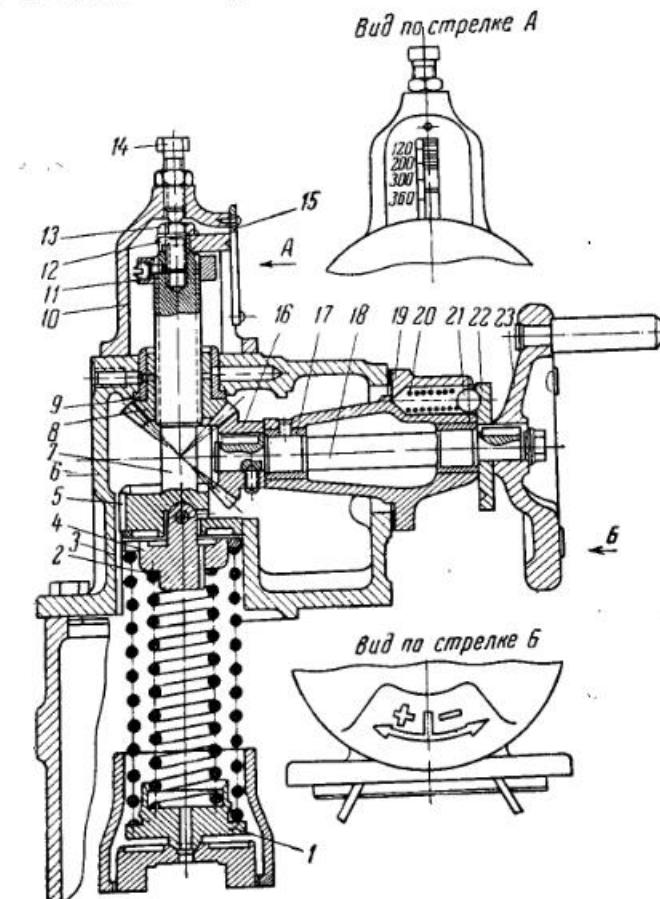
Пружинные весы регулятора числа оборотов двигателей типа NVD-36:
